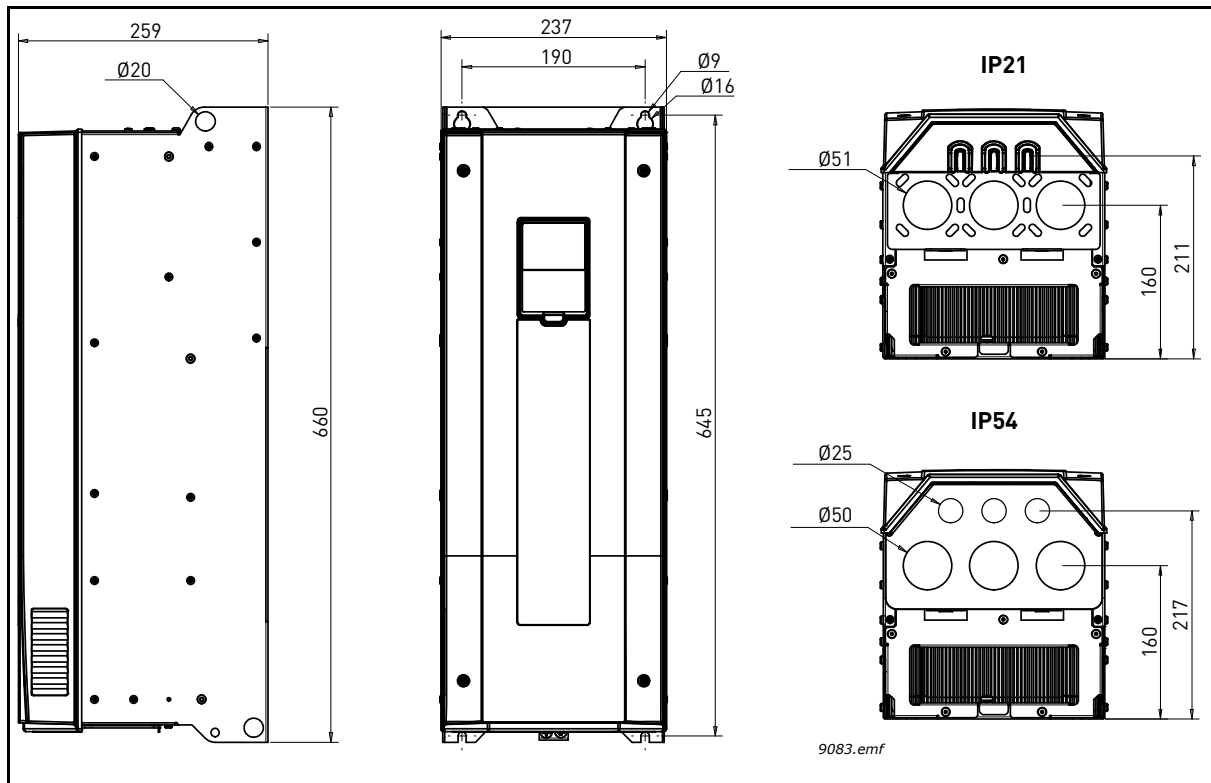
Dimensões do inversor de CA Vacon, MR7, montagem na parede
